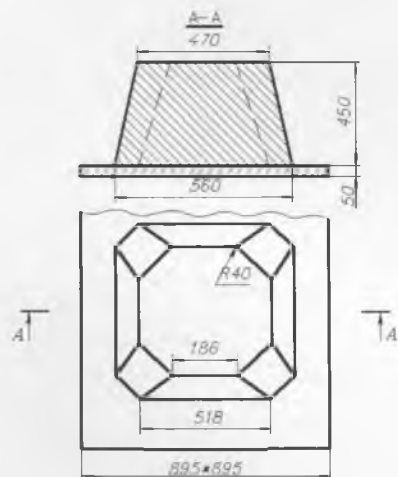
Шаблон для формирования рабочей поверхности футеровки
